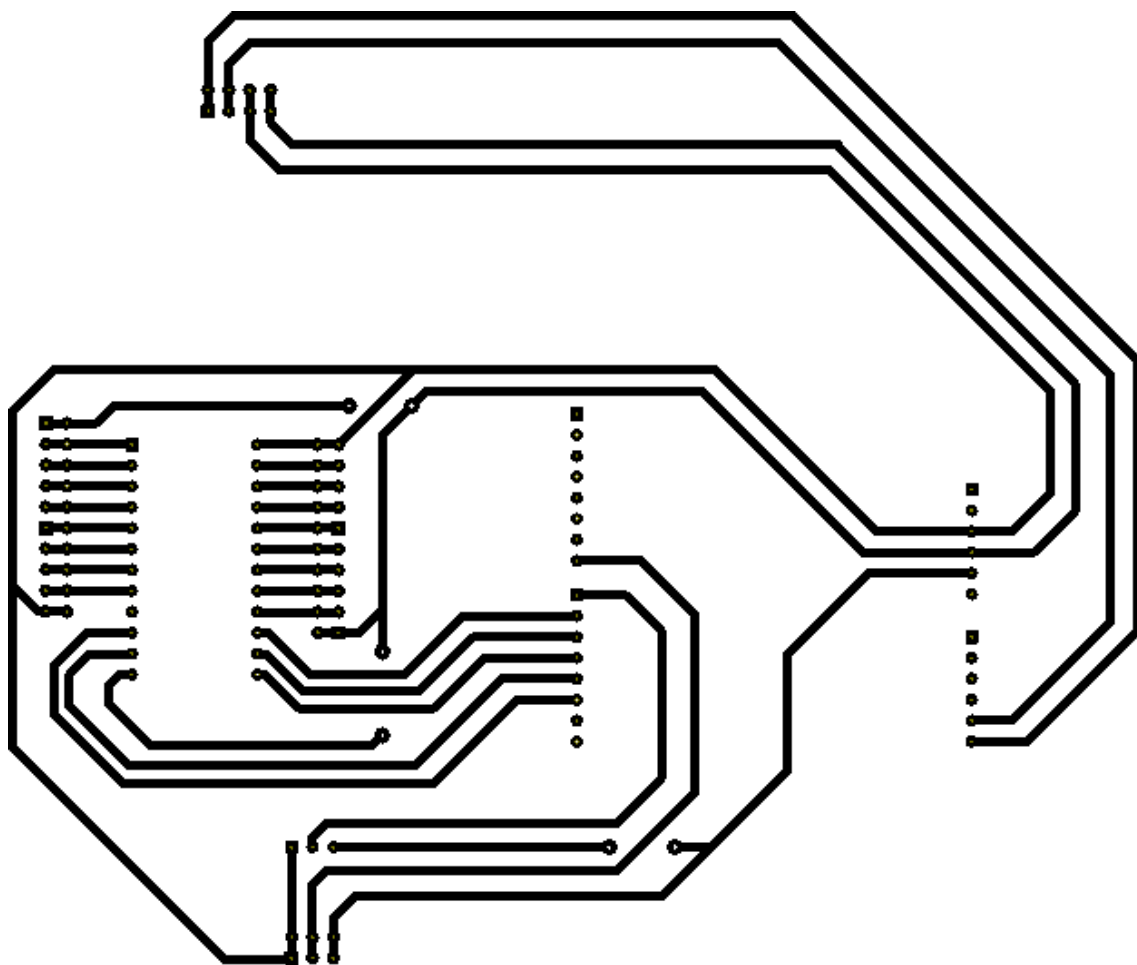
PCB Prototip principal (Impressió Placa Baquelita)
